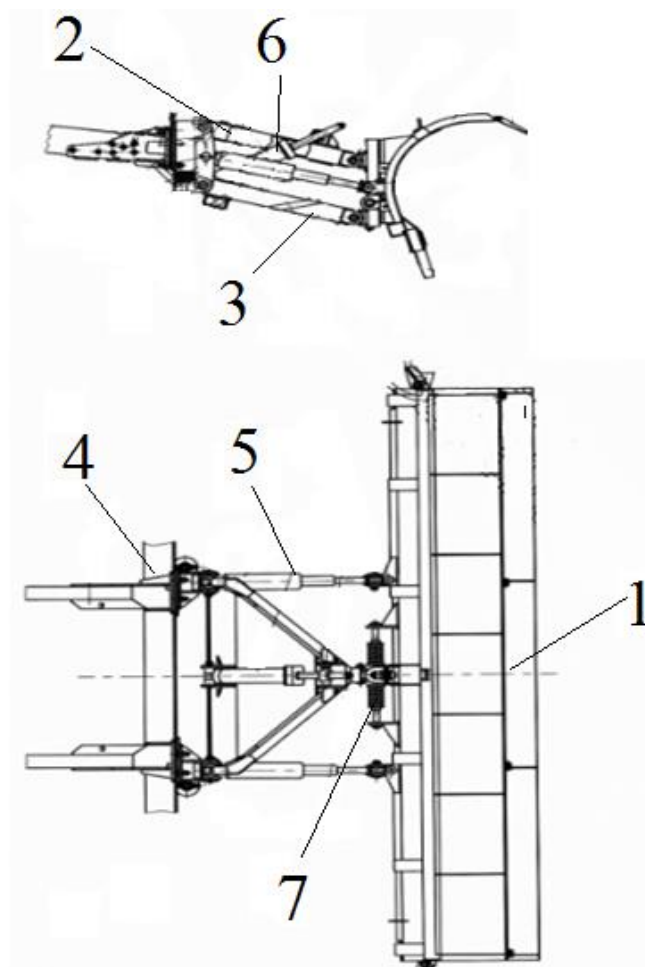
Отвал поворотный: 1 – лопата; 2 – шатун верхний;
